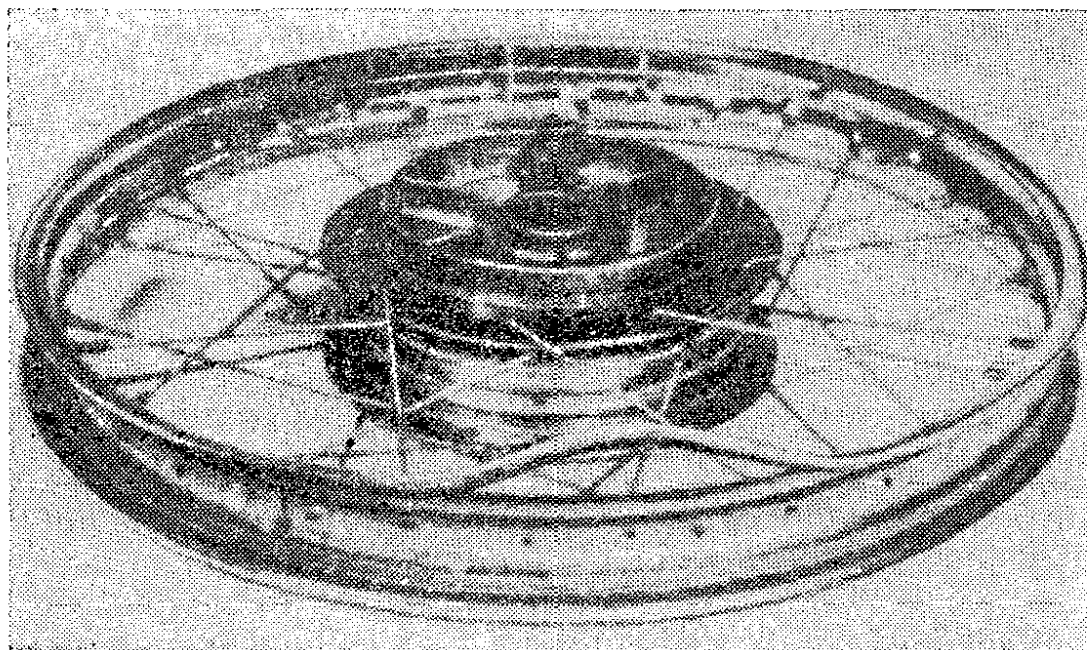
Общий вид левой стороны колеса мотоцикла. Видно отделение обода от остальной части колеса. Стрелкой указано положение сварного шва
